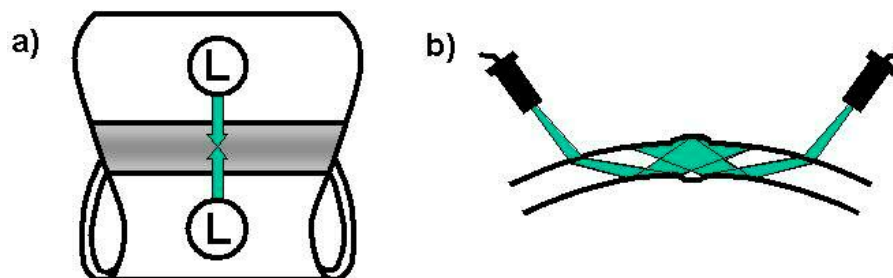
Nachweis von Längsfehlern. a) Draufsicht auf das Prüfkopfpaar mit Winkel-Einschallung und die Schweißnaht, b) Querschnittsansicht von Rohr und Prüfkopfpaar, hier zur Anzeige von Außenfehlern.
